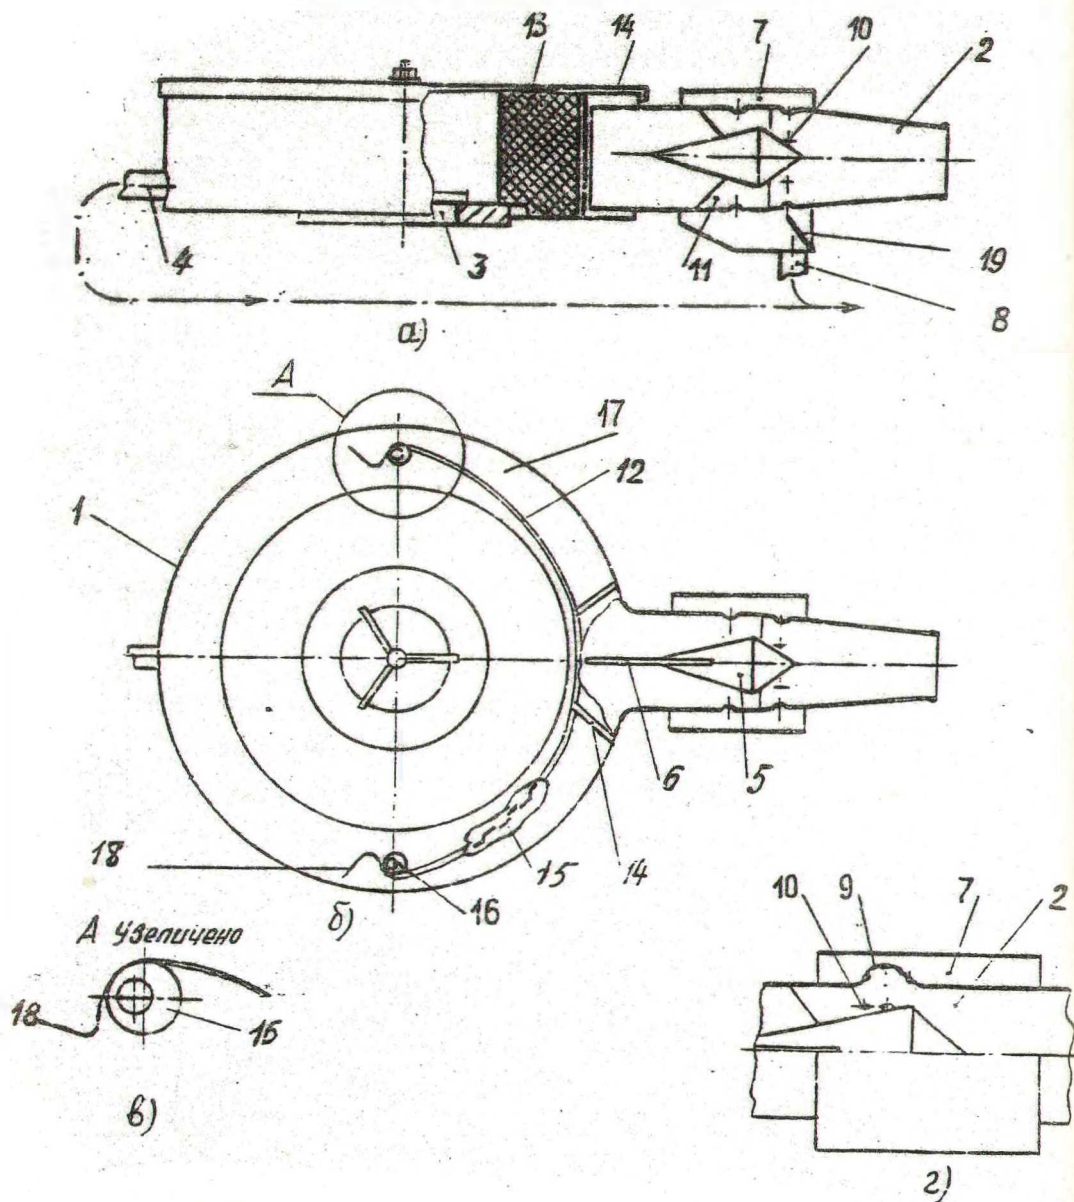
Рис. I. Регулируемый воздухоочиститель для двигателей автотранспортных средств
